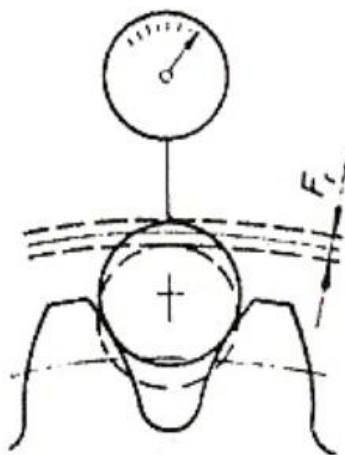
Místa kontroly házení ozubených kol po soustružení
